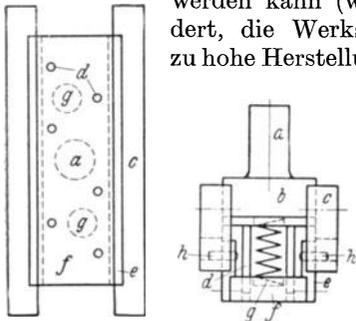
Bewegliche Schienenführung der Stempel für die Bearbeitung sperriger Werkstücke. Ansicht von unten und von vorn. *a* Zapfen nach DIN 810; *b* Stempelkopf; *c* Schienen; *d* Stempel; *e* Führungen für *f*; *f* bewegliche Stempelführungsplatte; *g* Federn für die Rückbewegung von *f*; *h* Anschlagstifte.
